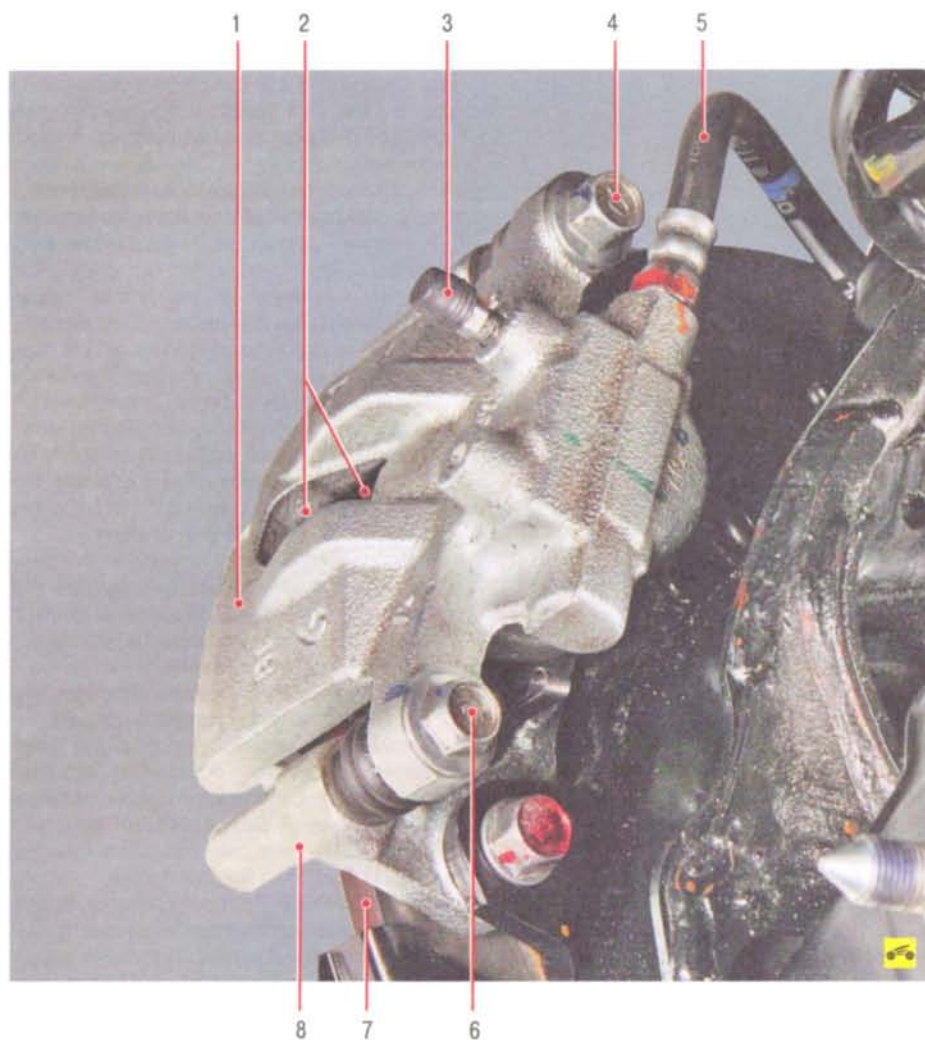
Детали заднего рабочего тормозного механизма: 1 — суппорт; 2 — тормозные колодки; 3 — клапан выпуска воздуха; 4 — верхний направляющий палец суппорта; 5 — тормозной шланг; 6 — нижний направляющий палец суппорта; 7 — тормозной диск; 8 — направляющая тормозных колодок
